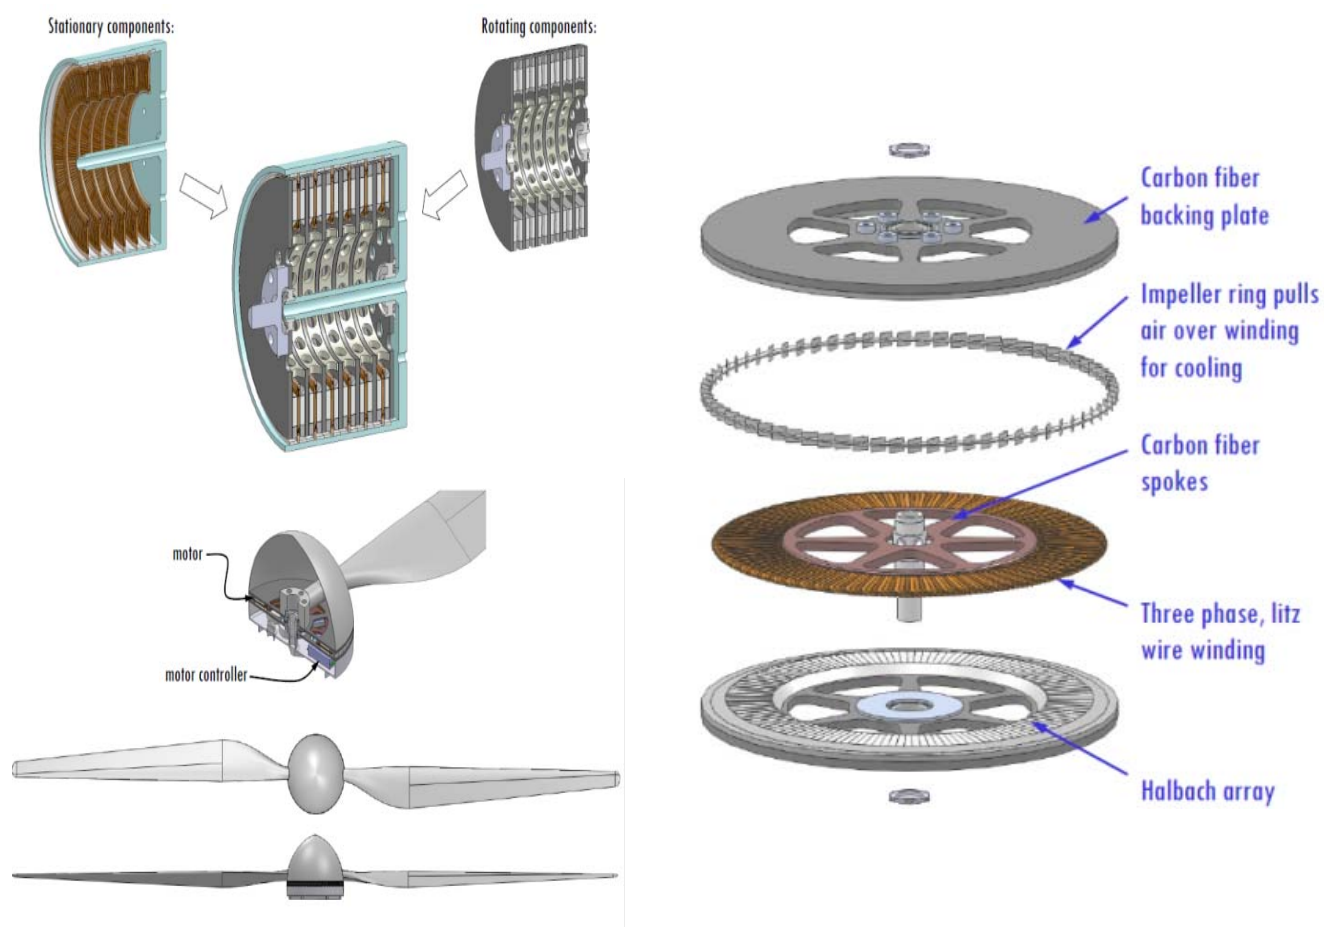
Схема и внешний вид двигателя *LaunchPoint Technologies
